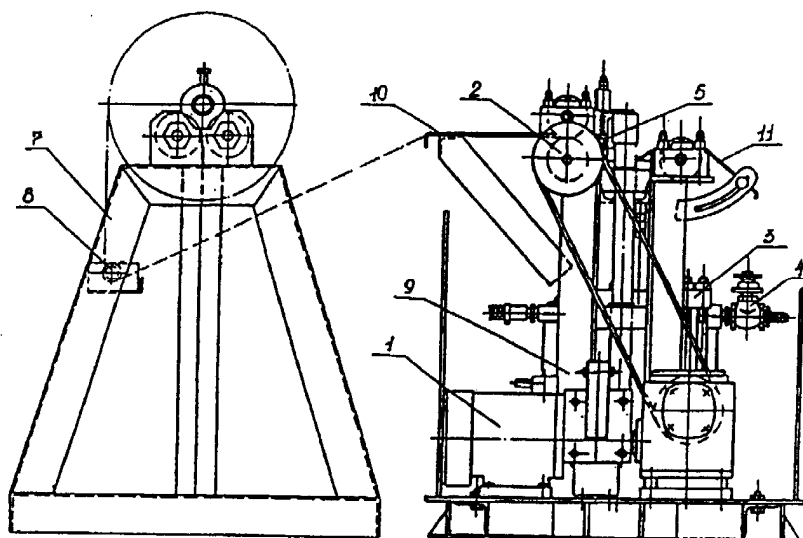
Полуавтомат для изготовления пакетов ПАСП-700
